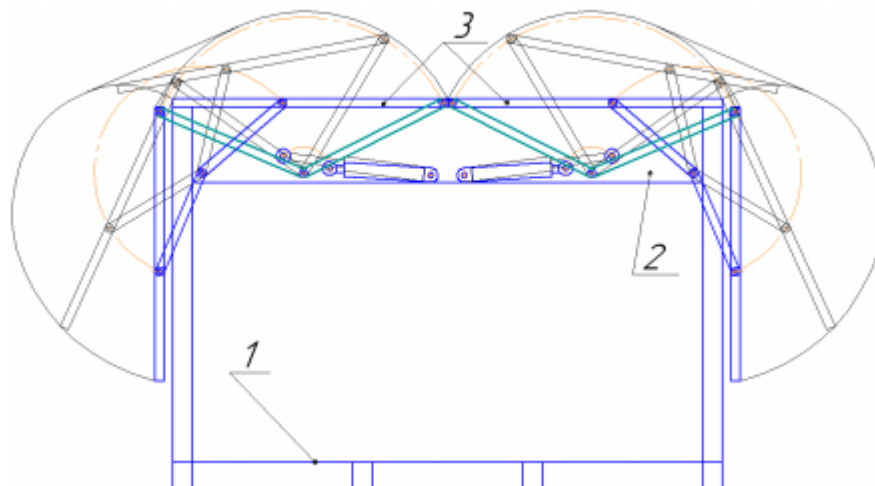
Схема роботи рухомого даху зерновозу: 1 – кузов; 2 – наставка бічного борту; 3 – рухомий дах
